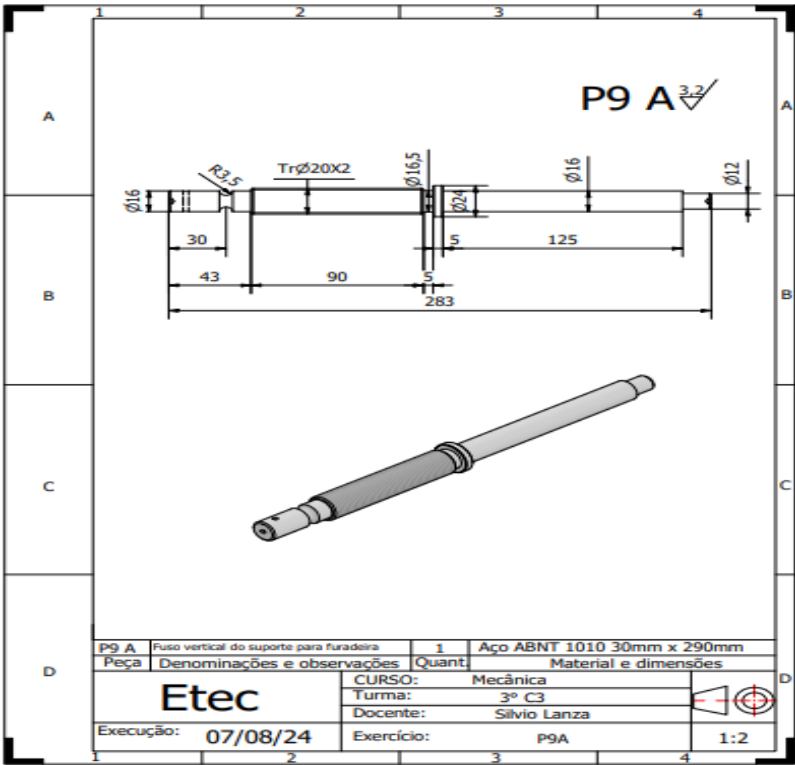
P9A: Fuso vertical do suporte para furadeira;
